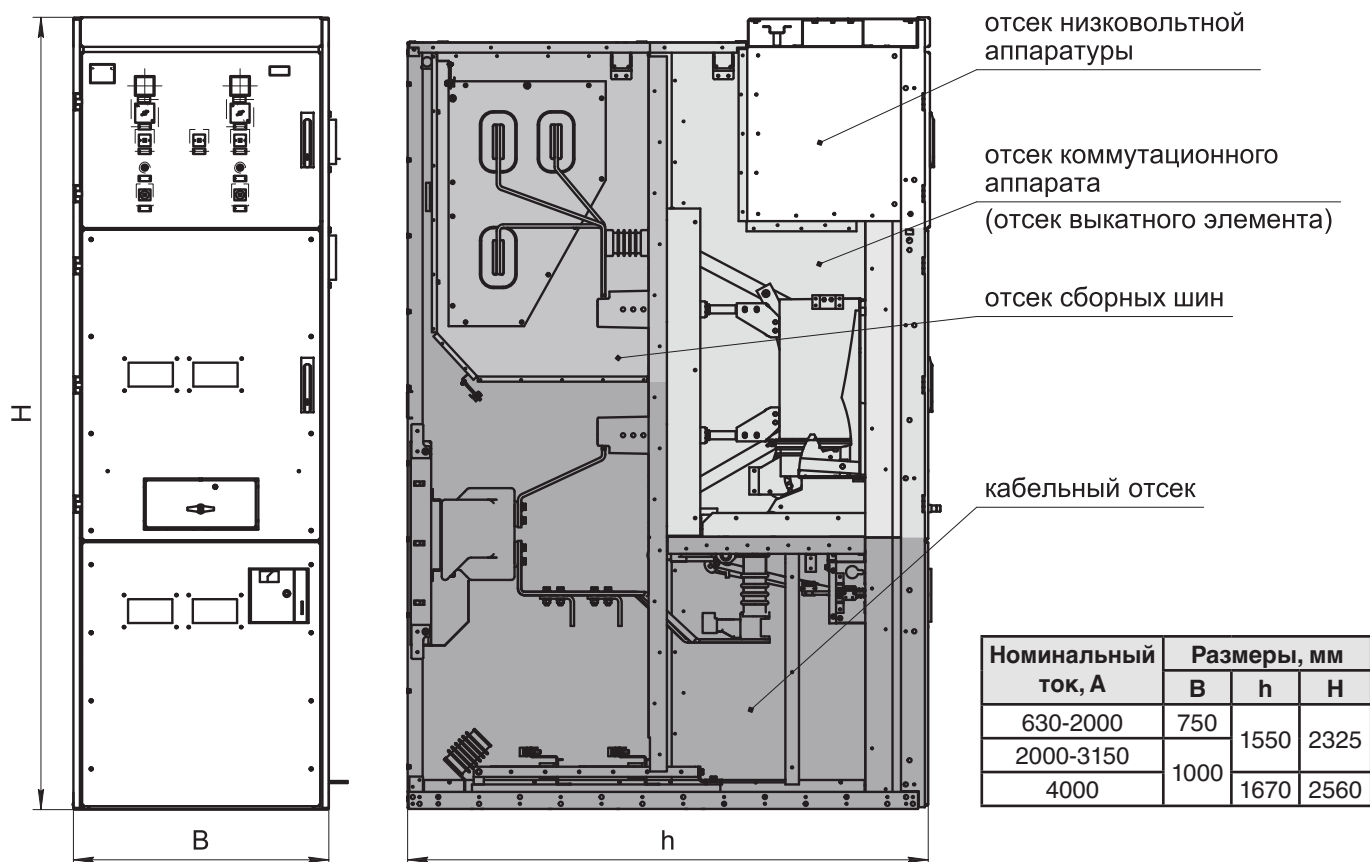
Габаритные размеры шкафа КМП-С с выключателем.
